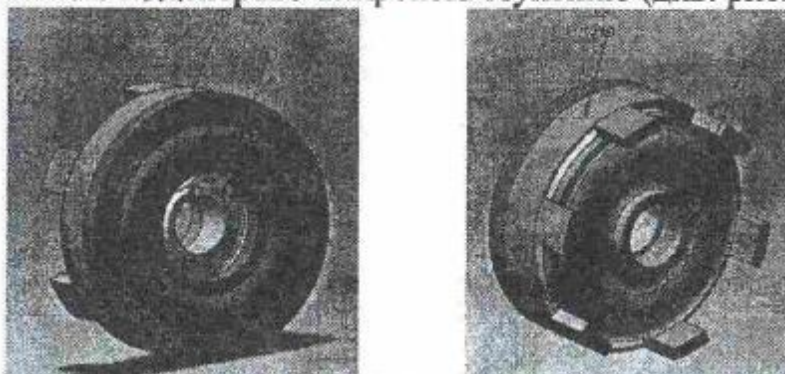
Загальний вид ступені: 1 – РК; 2 - передня вихрова ступень; 3 - задня вихрова ступень; 4 – корпус РК.
